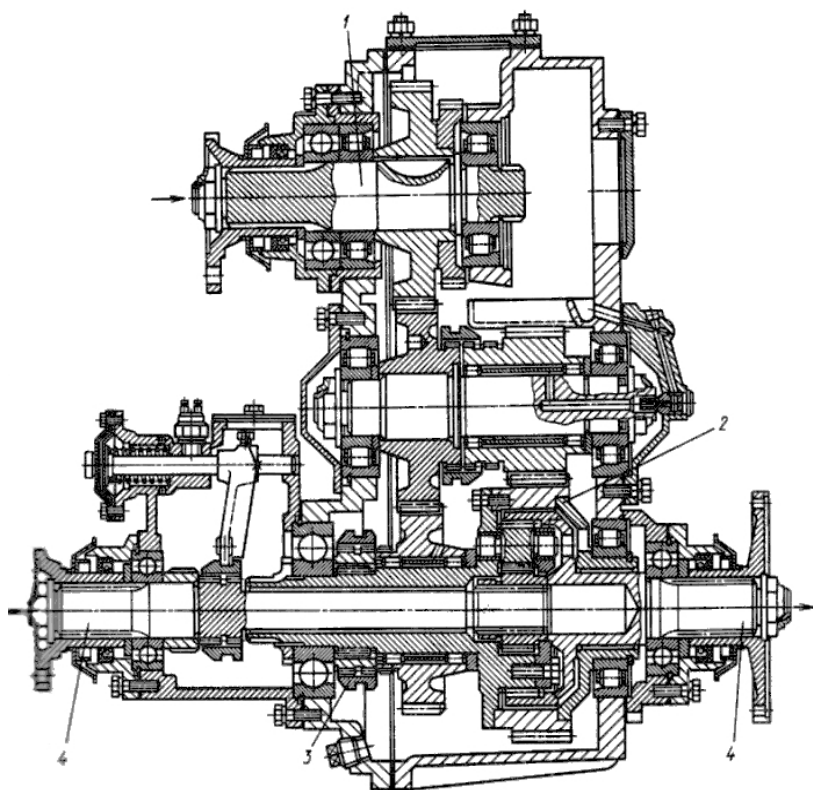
Конструкция раздаточной коробки с несимметричным межосевым дифференциалом автомобиля КАМАЗ-4310
